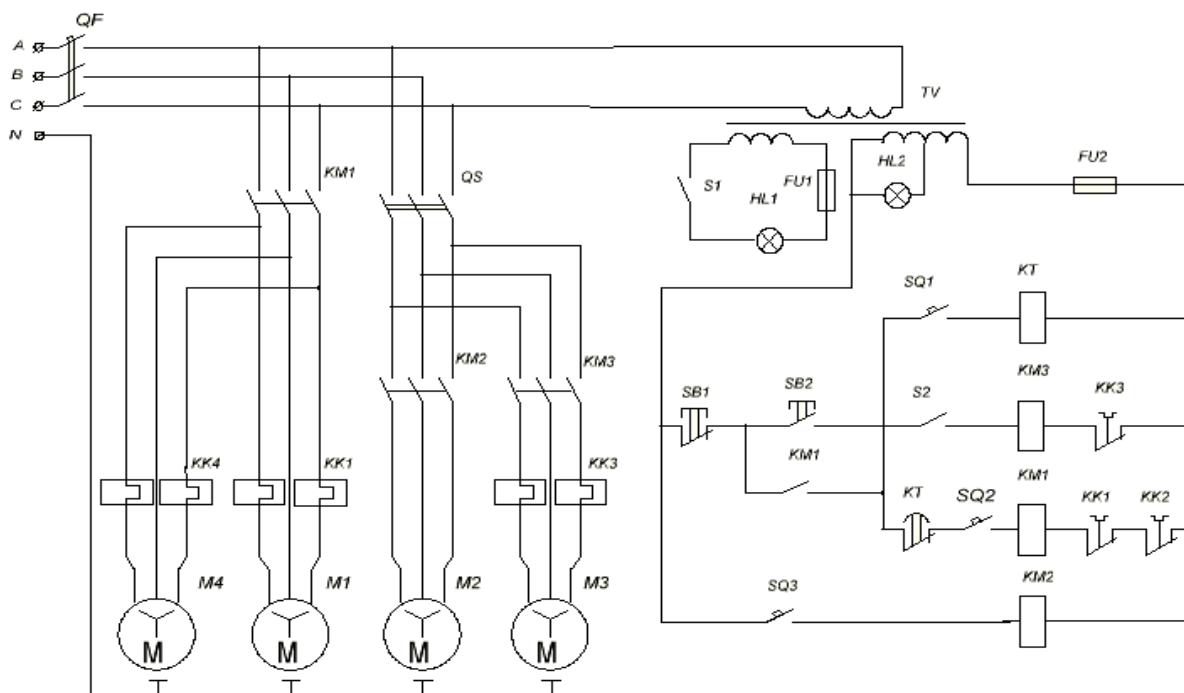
Електрична принципова схема токарного верстата 9CRAFT WM210V
